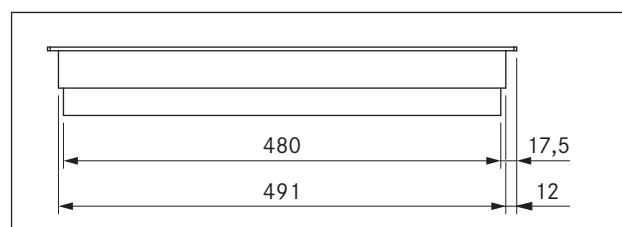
CKCB dimensioni apparecchio vista laterale
